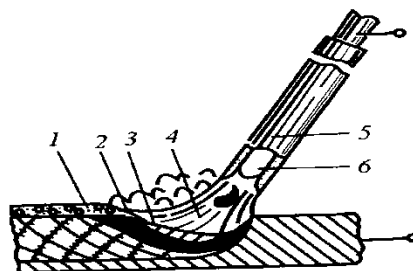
Схема ручного дугового зварювання покритим електродом:
